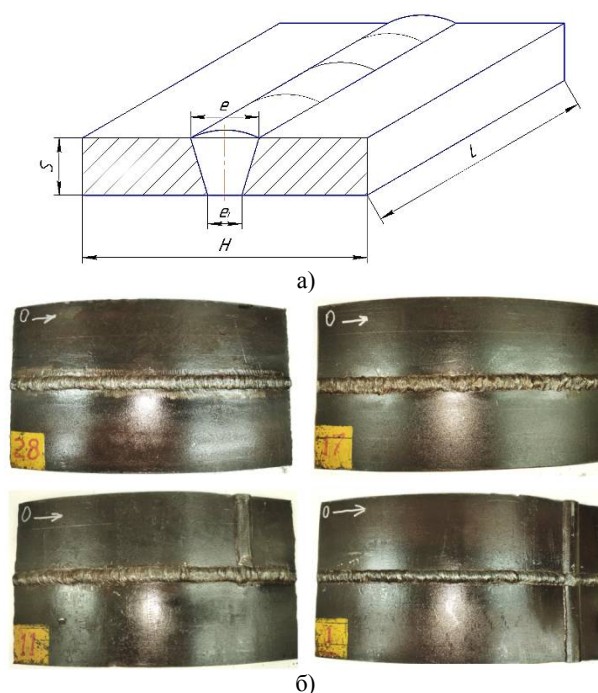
Исследуемые образцы: а) эскиз сварного соединения, б) вид исследуемых образцов
